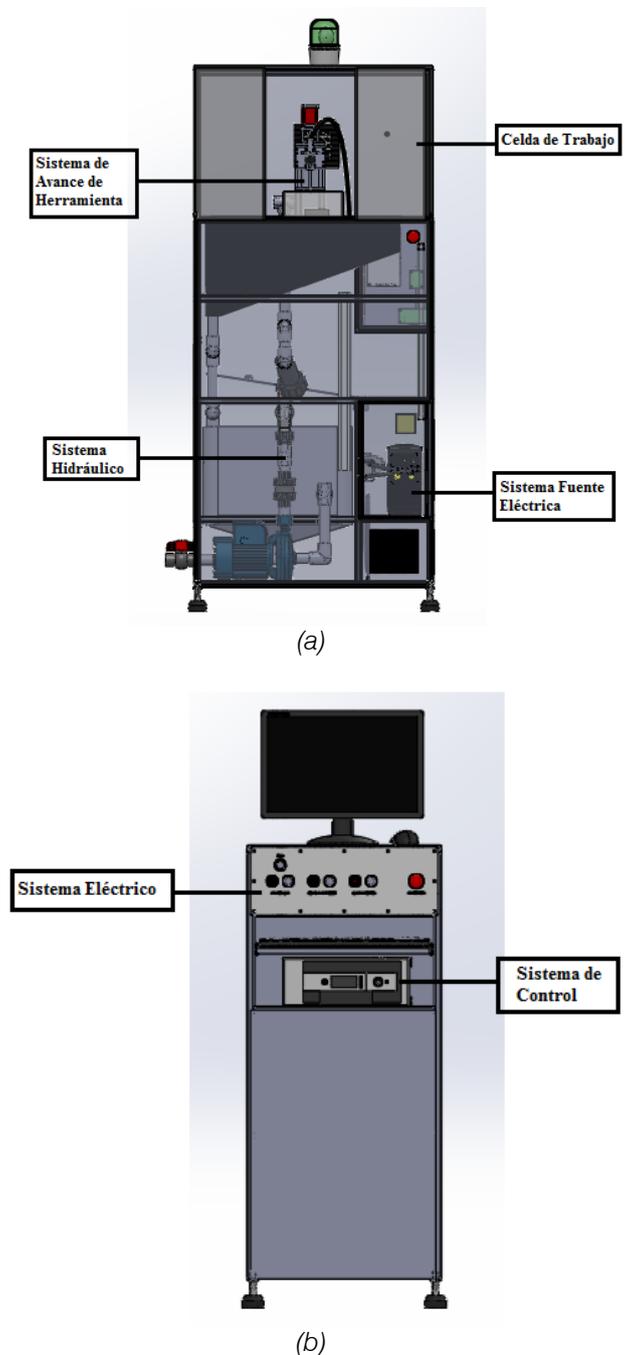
ESQUEMA MÁQUINA DE ECM; a) Módulo de Maquinado; b) Módulo Controlador
